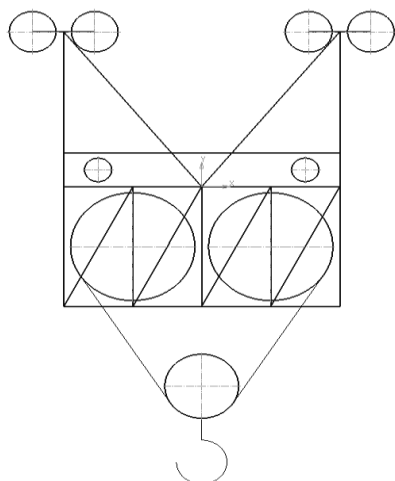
Расчётная схема тележки кабель-крана ферменной конструкции
